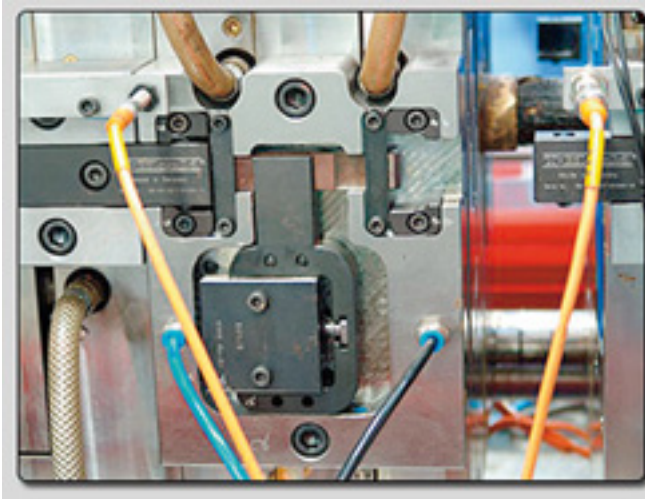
Teilansicht eines Tandemwerkzeugs; Düsenseite geöffnet [13.18]
